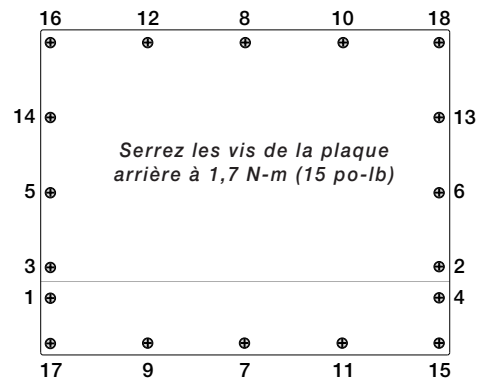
Plaque arrière de boîtier d'indicateur 820i et 920i
